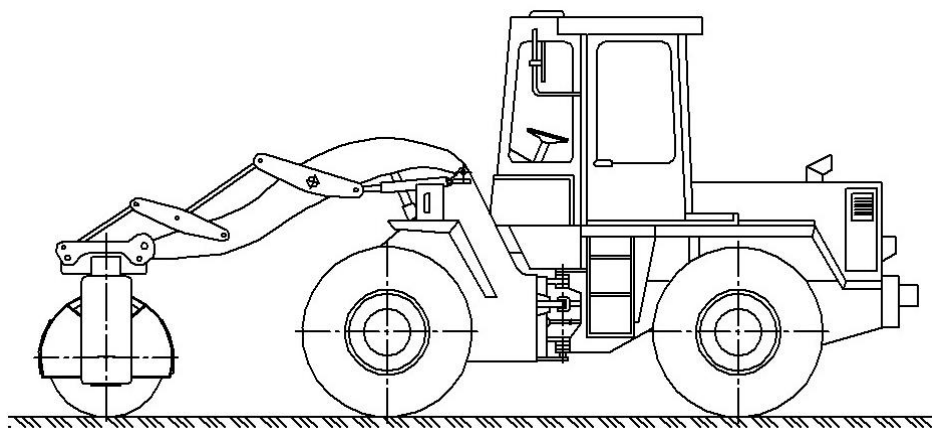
Вариант крепления уплотняющего рабочего оборудования к фронтальному погрузчику
